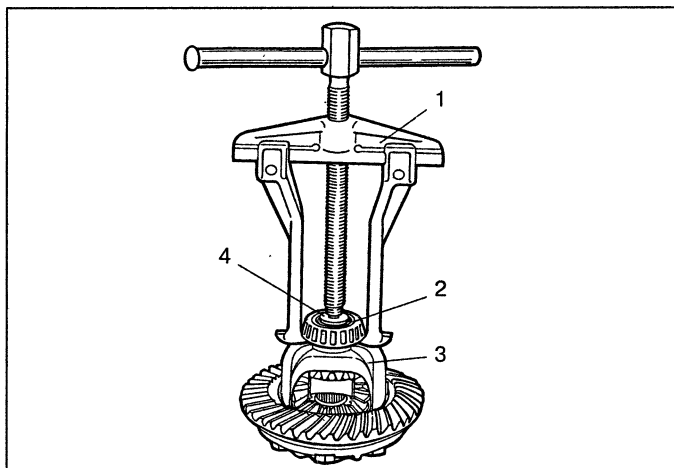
Снятие внутреннего кольца заднего подшипника ведущей шестерни универсальным съемником А.40005/1/7: 1 – универсальный съемник; 2 – ведущая шестерня; 3 – кольцо подшипника; 4 – приспособление А.45008
